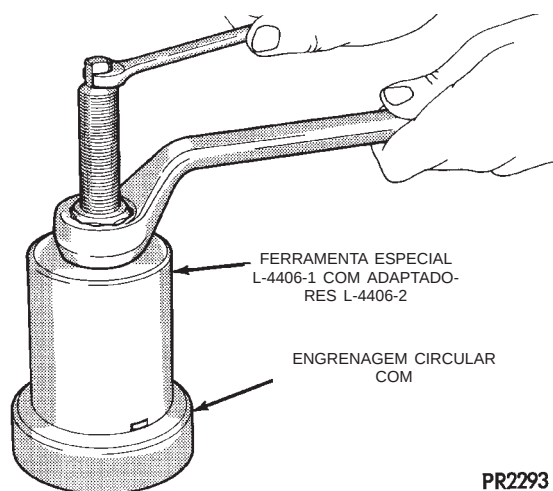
Remoção do Cone de Rolamento da Engrenagem Circular Traseira com Dentes Interiores
